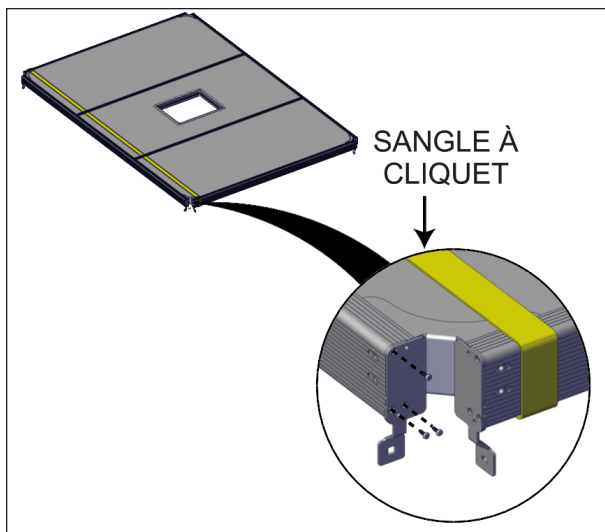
INSTALLATION DES SANGLES SUR LES PANNEAUX
